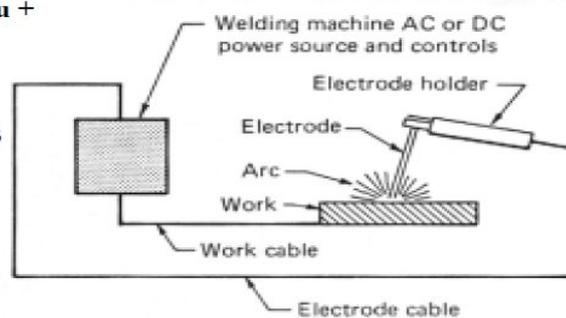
soldadura a ER. Fonte - Altino Loureiro
